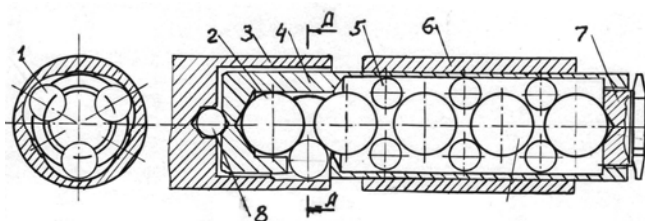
Механізм закріплення заготовок типу «втулка»
